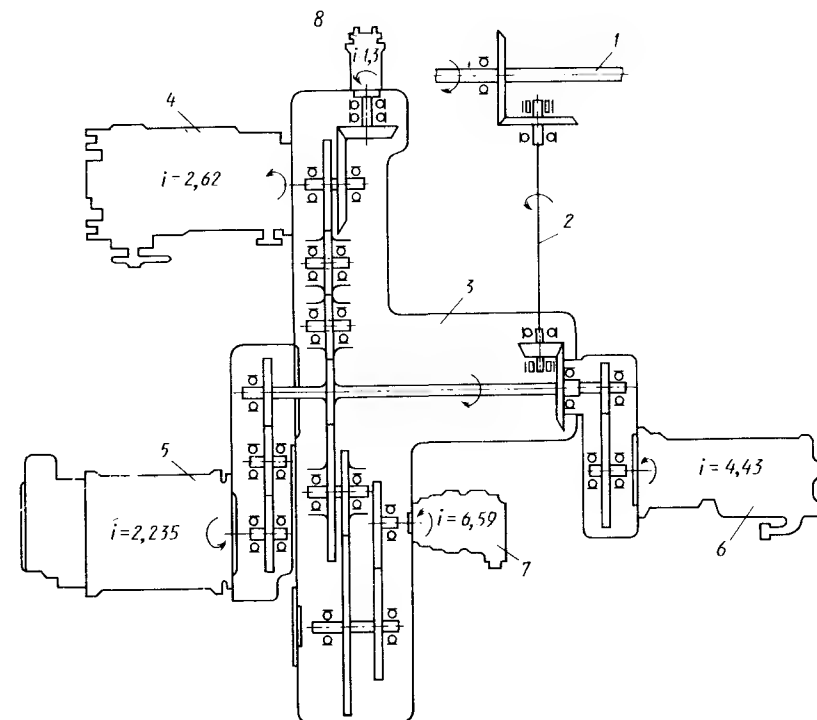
Кинематическая схема привода агрегатов одновального двигателя: 1 — ротор двигателя; 2 — привод коробки агрегатов; 3 — коробка агрегатов; 4 — топливный насос; 5 — электростартергенератор; 6 — масляный агрегат (насосы); 7 — датчик тахометра; 8 — центробежный суфлер
